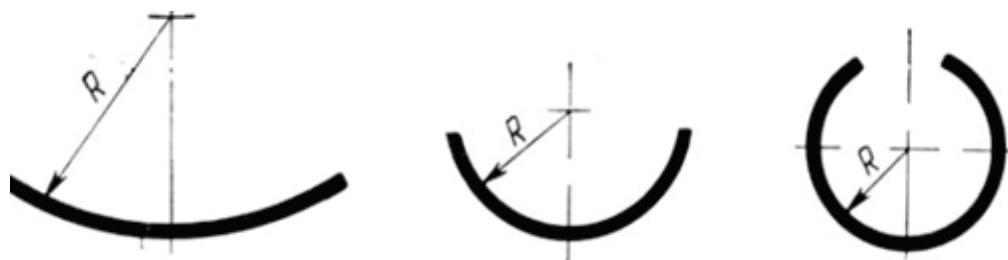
Типы калибровок инструмента для формовки трубной заготовки
